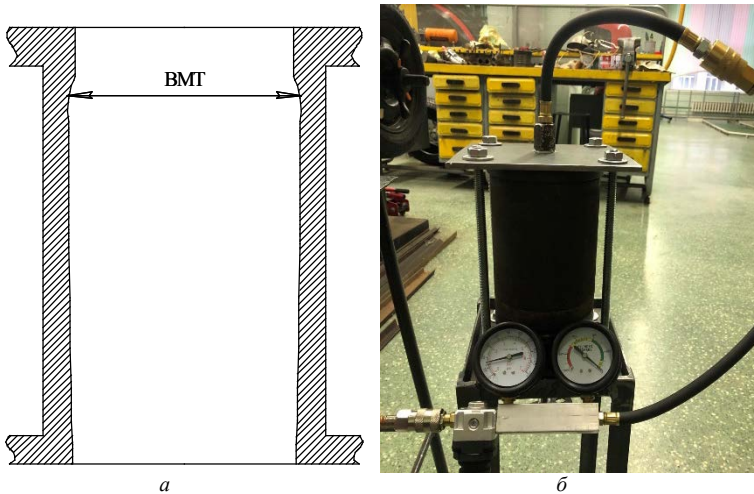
Схема износа цилиндра двигателя (а) и лабораторная установка для исследования пневмоплотности цилиндропоршневой группы (б)
